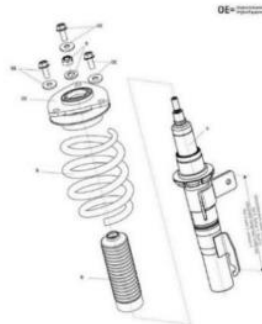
Proceso de montaje de la suspensión trasera. [Instrucciones de montaje del kit]
